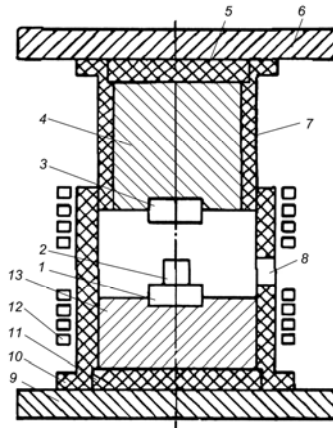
Принципова схема штампового блоку для ізотермічного штампування
